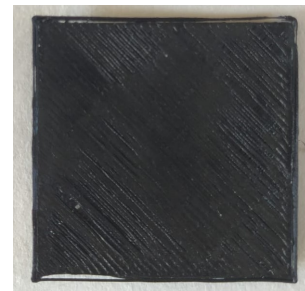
Placa impresa boq.0,4mm, ep=0,8mm
